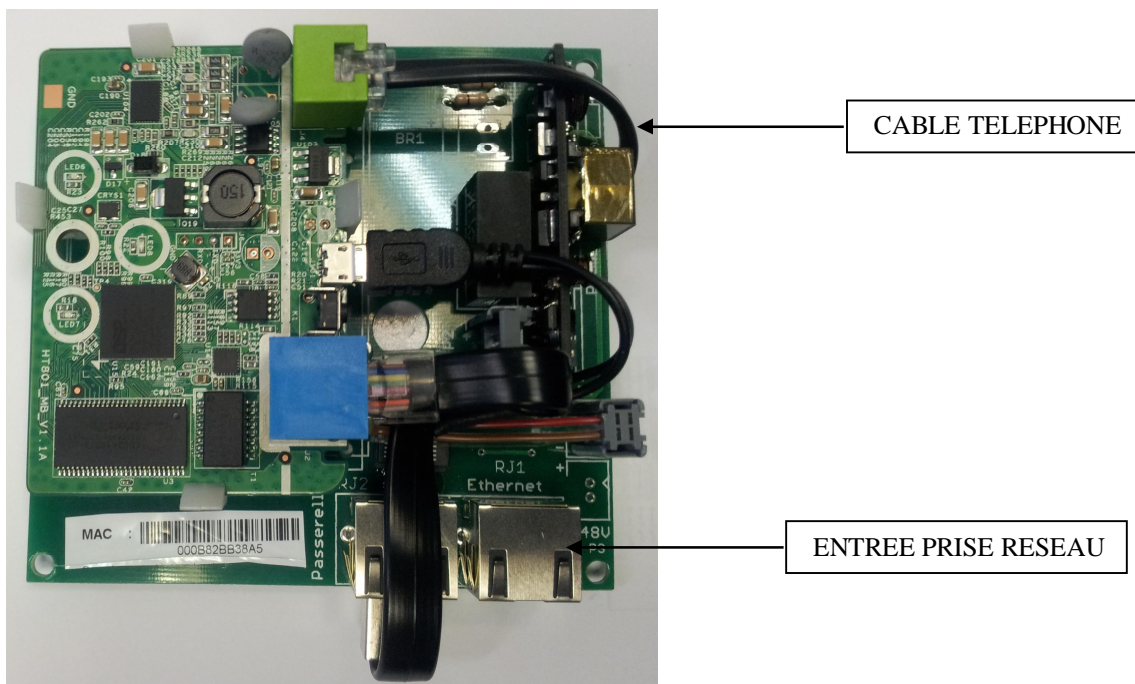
Ensemble carte SIP/VOIP/PoE - Réf.: MT302SIP-POE.
